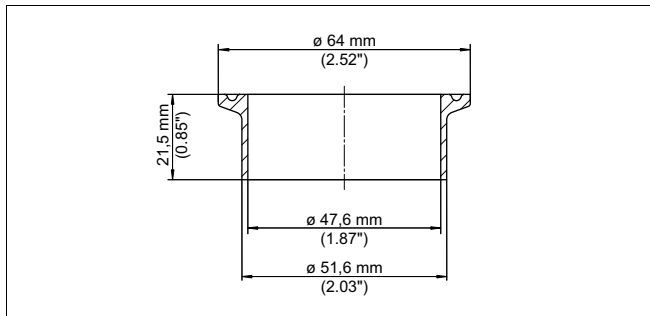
Medidas da luva soldada Clamp 2" PN16 (ø 64 mm) DIN 32676, ISO 2852/316L
